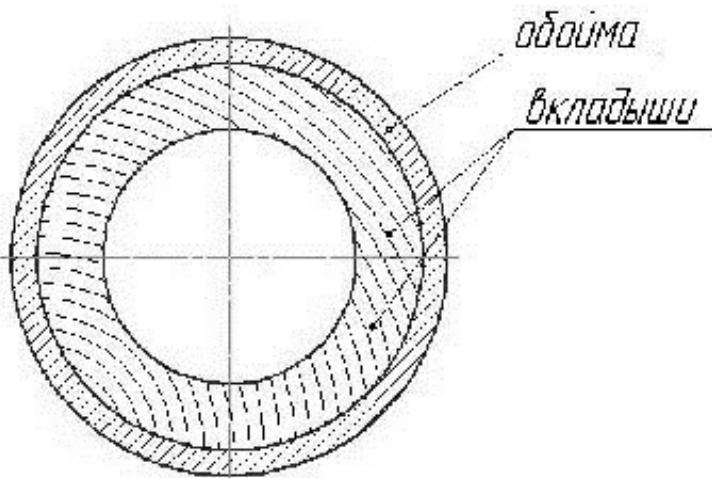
Двухслойная модель подшипника скольжения с древесно-металлическим вкладышем
